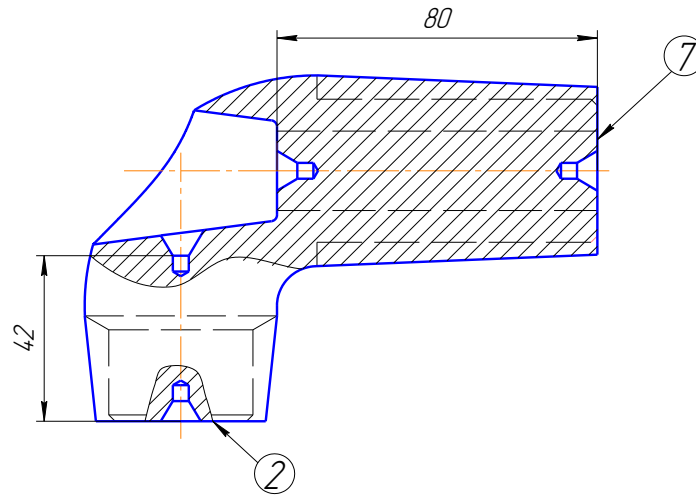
Операційний ескіз фрезерно-центрувальної операції
